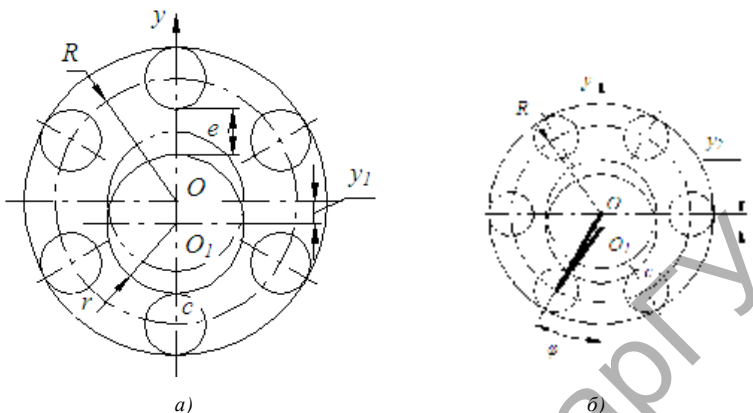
Схема расположения внутреннего кольца подшипника
